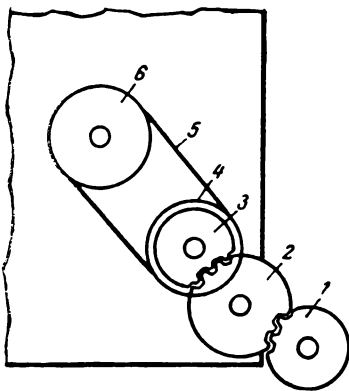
Кинематическая схема связи устройства с механизмом проявочной машины
